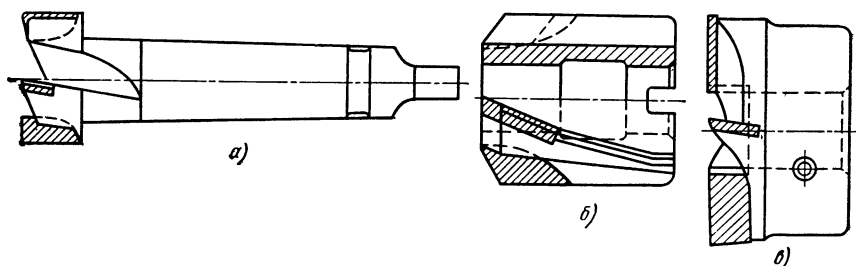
Зенкеры, оснащенные пластинками из твердого сплава
